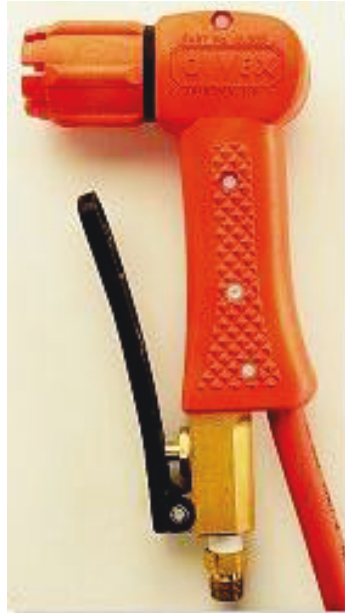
Umbilical para corte y soldadura. Fuente: jmbuzos@arnet.com
